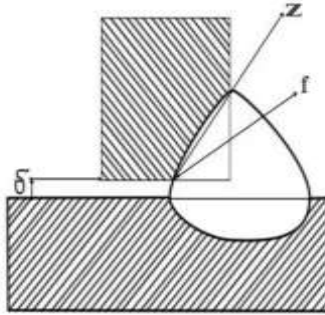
Поперечное сечение углового шва в тавровом соединении
